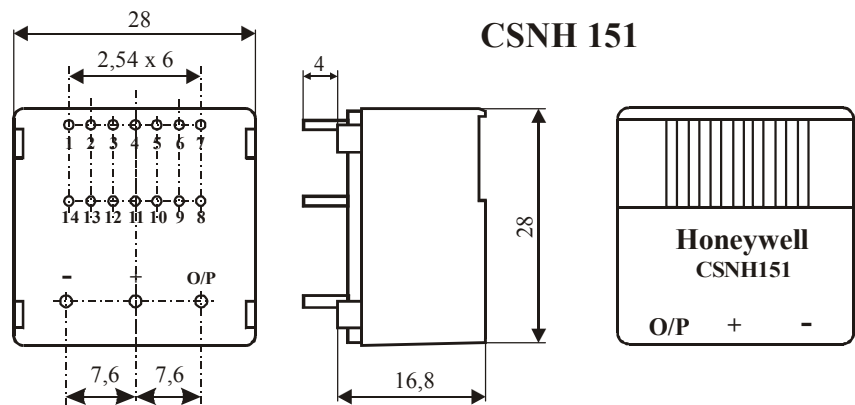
Внешний вид и габаритные размеры датчиков тока типа CSNH-151
